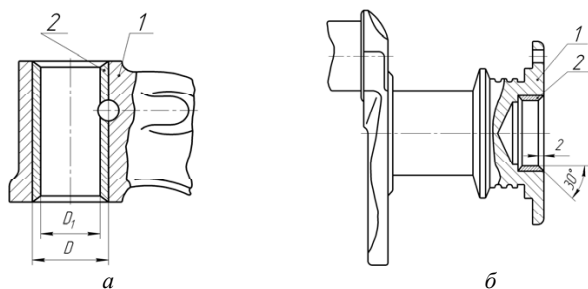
Схемы восстановления деталей дополнительными ремонтными деталями (*a* – втулкой; *б* – кольцом): 1 – восстанавливаемая деталь; 2 – дополнительная ремонтная деталь
